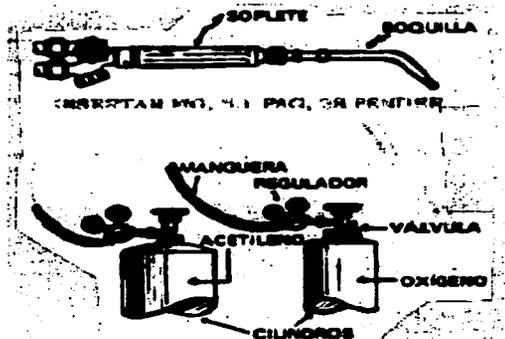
EQUIPO BÁSICO PARA SOLDADURA CON OXIACETILENO.
